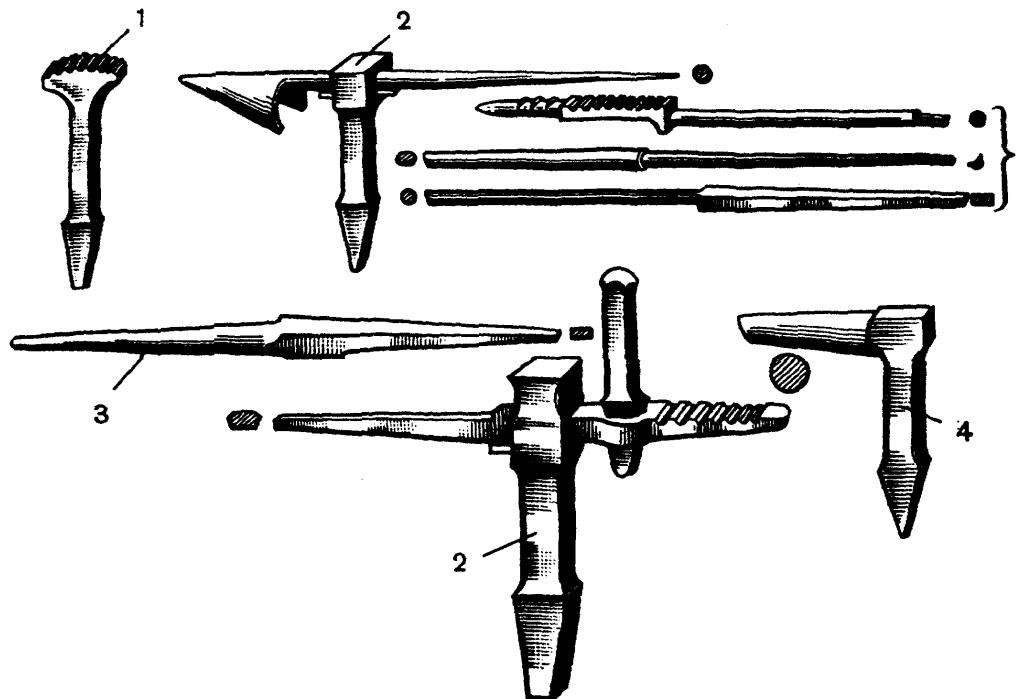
Различные виды шпераков и приспособлений к ним:
